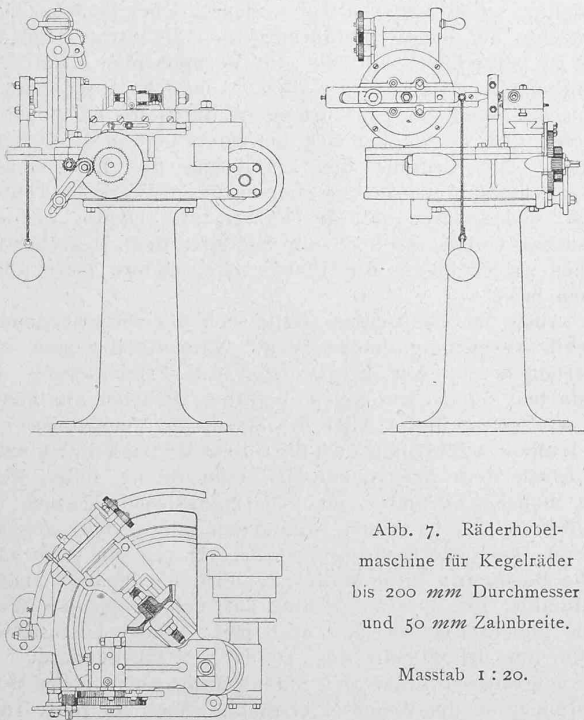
Räderhobelmaschine für Kegelräder bis 200 mm Durchmesser und 50 mm Zahnbreite.
